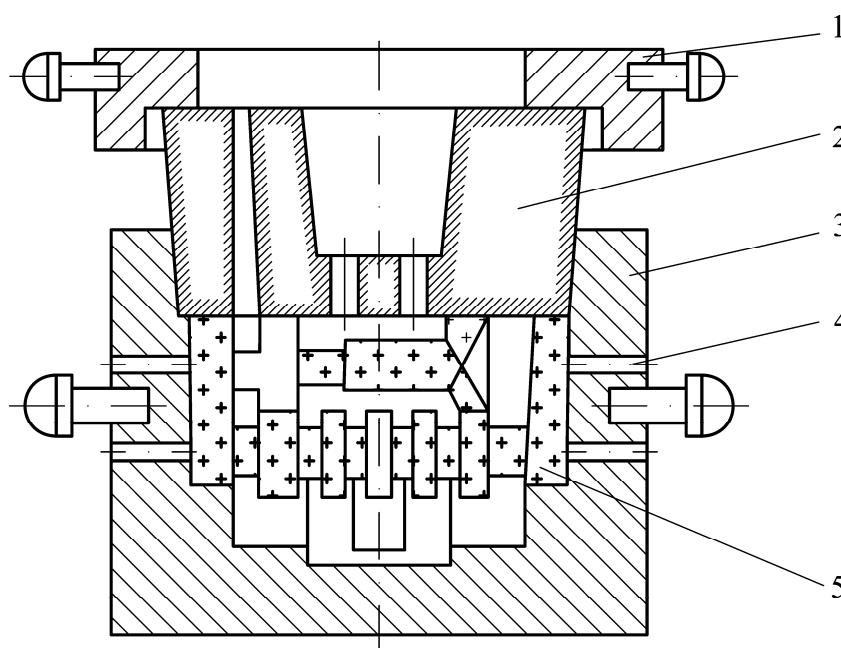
Вытряхной кокиль: 1 – груз; 2 – песчаная чаша; 3 – кокиль; 4 – вентиляционный канал; 5 – песчаный стержень
